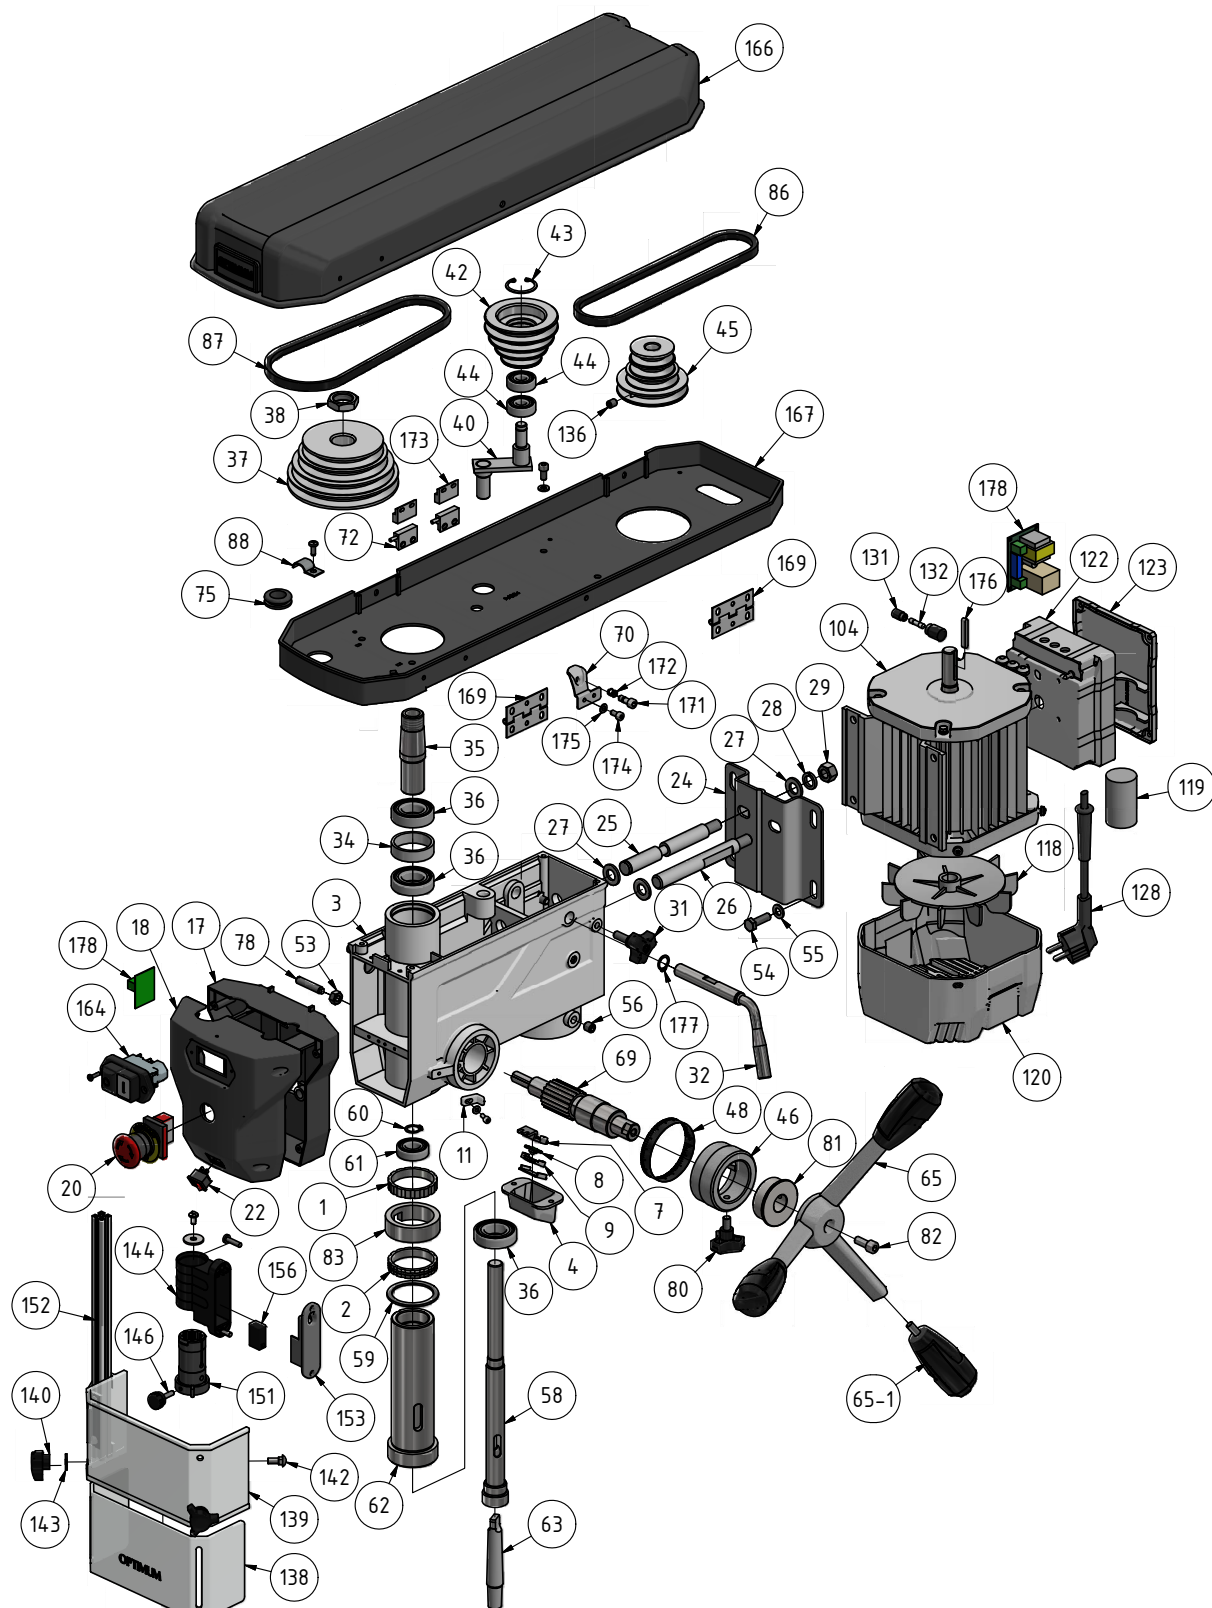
DQ22 - Bohrkopf - Drill head
